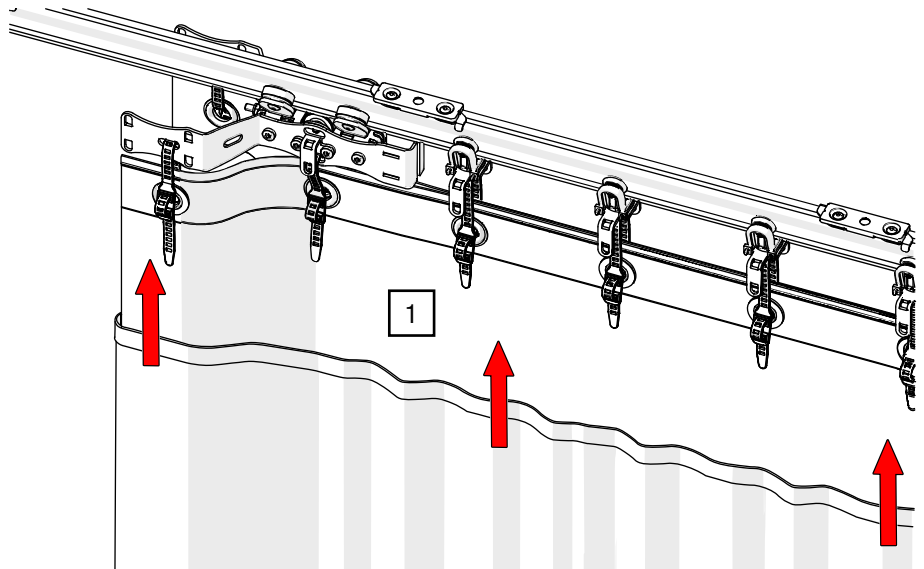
Zugwagen mit doppeltem Überzugbügel – Außenlagen anheben und positionieren (1/2)
